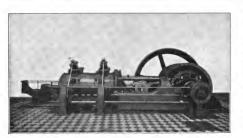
Gasmaschine der Maschinenbau-Akt.-Ges. Union in Essen-Ruhr.
